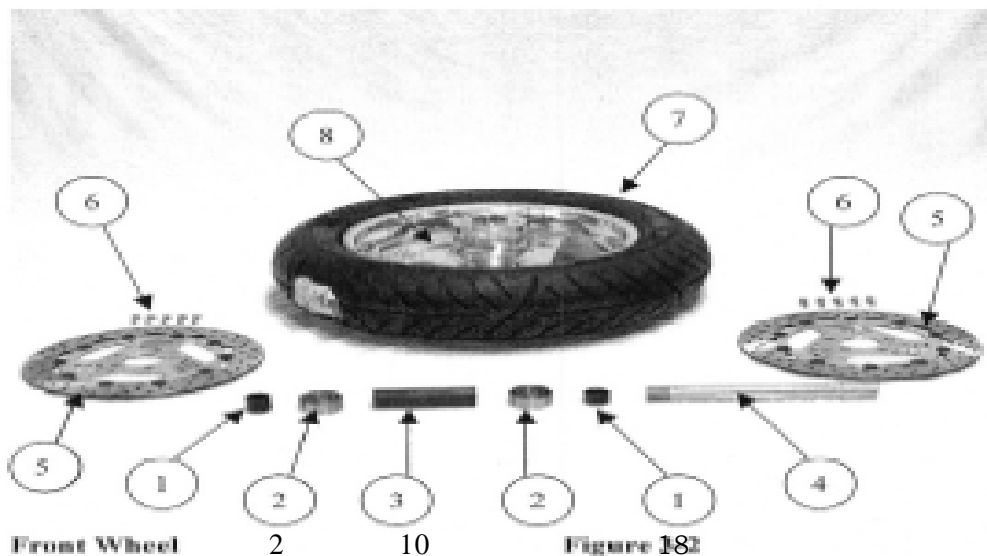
Zeigt die Radachse und Kolben demontiert.
